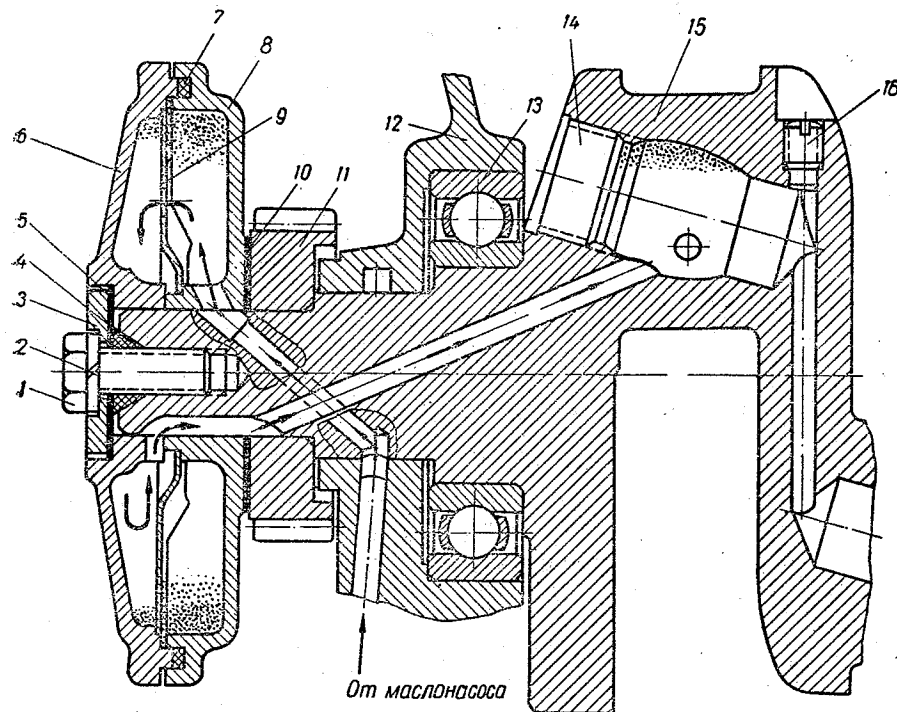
Центрифуга и передний коренной шарикоподшипник:
